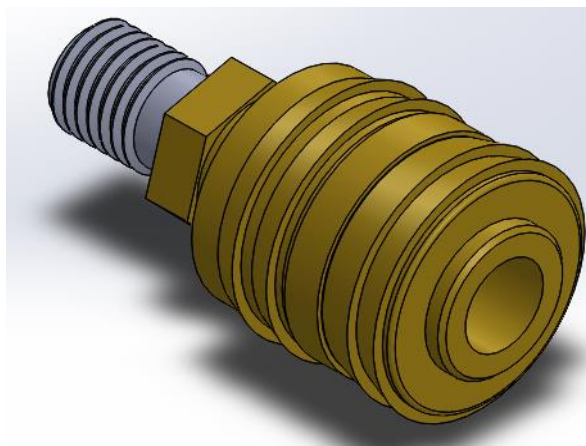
CAD model – Průchodka z pozinkované oceli
